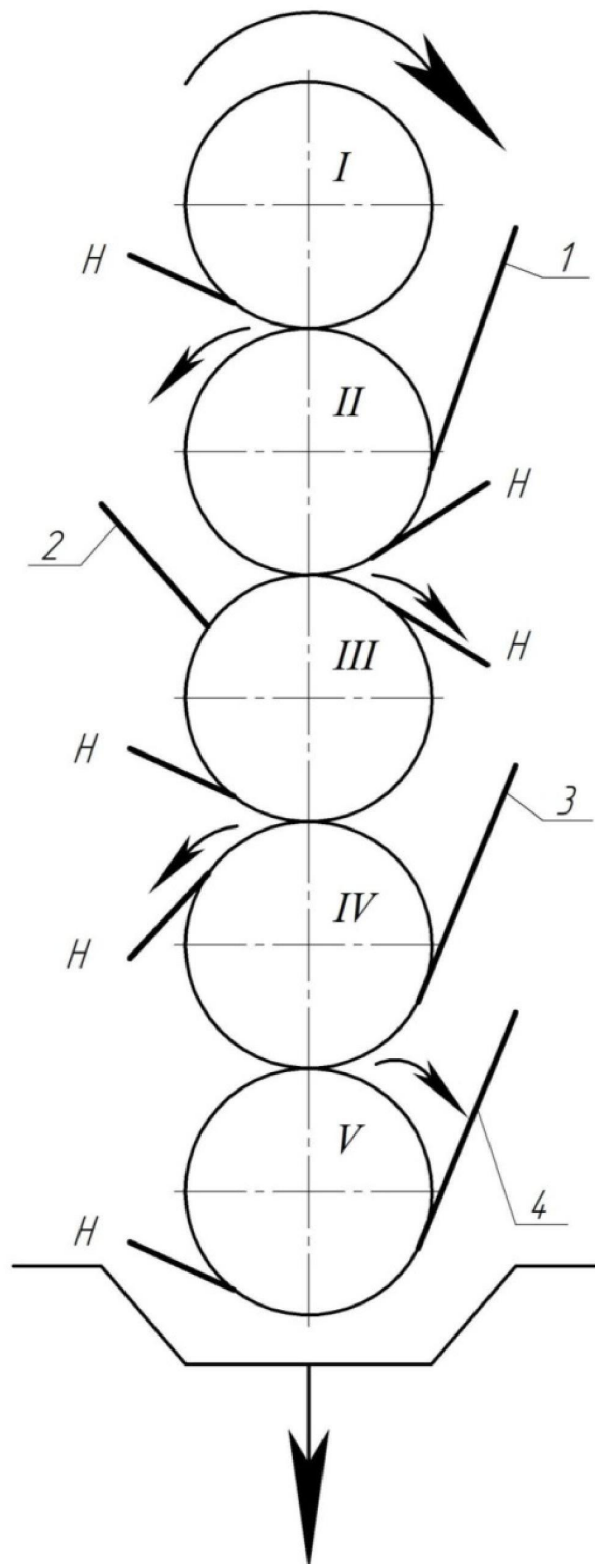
Схема розташування щитів і ножів п'ятивальцевого верстата:
